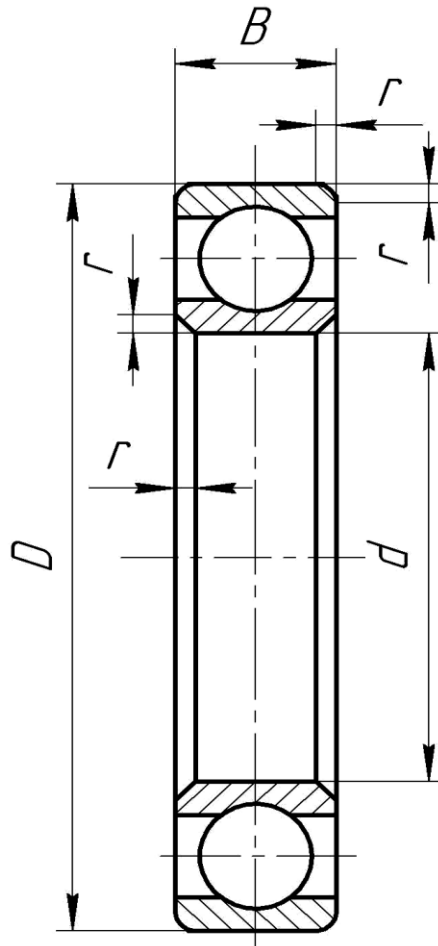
Эскиз подшипника (ГОСТ 23179–78)
